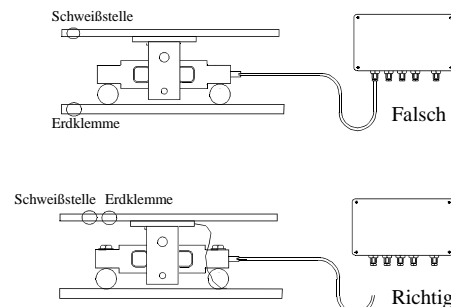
Elektroschweißen nach dem Einbau der Wägezellen.
